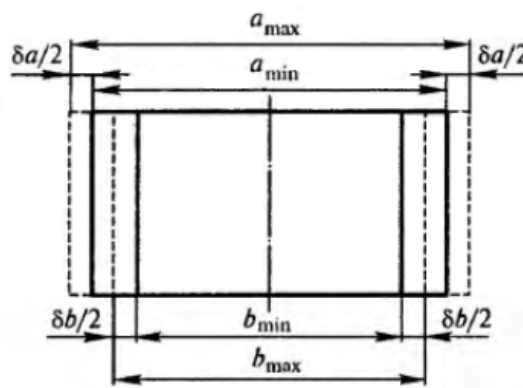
Схема для визначення граничних розмірів під час оброблення зовнішньої циліндричної поверхні
